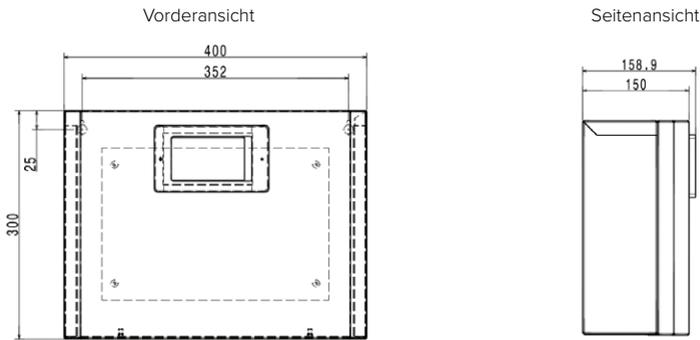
Außenabmessungen des Gehäuses der Steuerung
